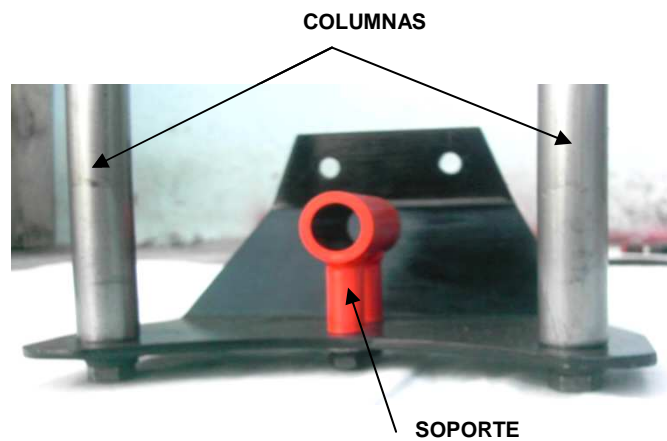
MONTAJE DE COLUMNAS, SOPORTE Y PLATO INFERIOR
